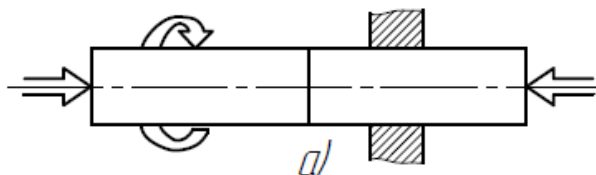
Схема соединения деталей при сварке трением
